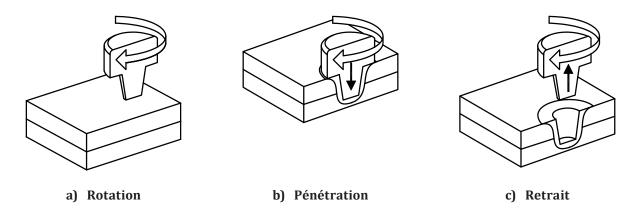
Principe de base du soudage par friction-malaxage par points
